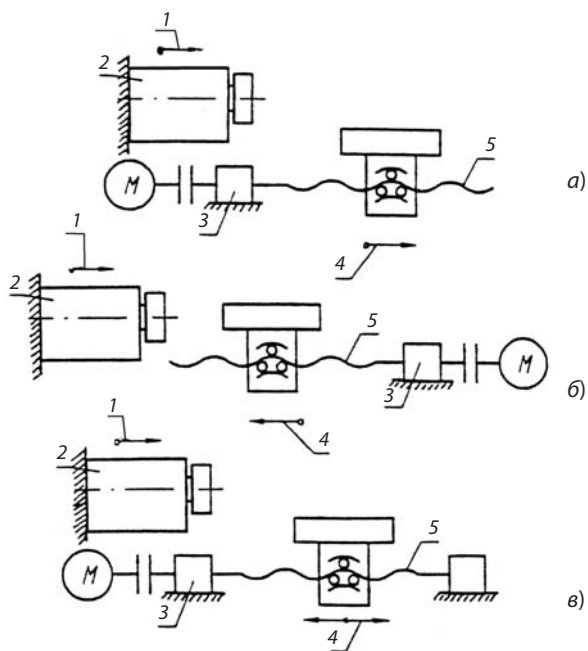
Виды компоновок привода продольной подачи суппорта токарного станка с ЧПУ:
